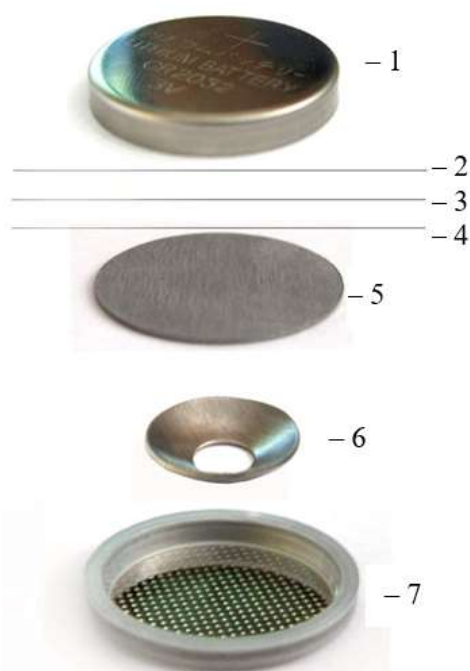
Схема сборки ячеек в корпусах CR2025: 1 – катодный контакт корпуса; 2 – катод; 3 – сепаратор; 4 – анод; 5 – прокладка из нержавеющей стали; 6 – пружина; 7 – анодный контакт корпуса
